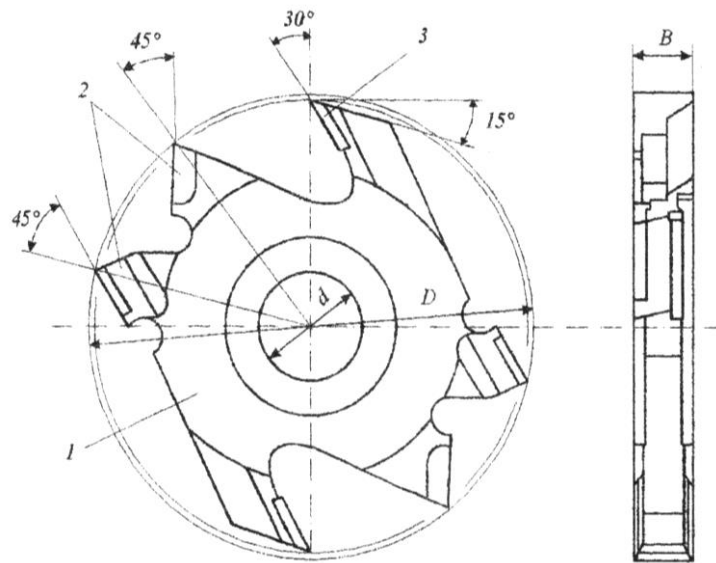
Конструкція пазової фрези типу 2 для фрезування поперек волокон
